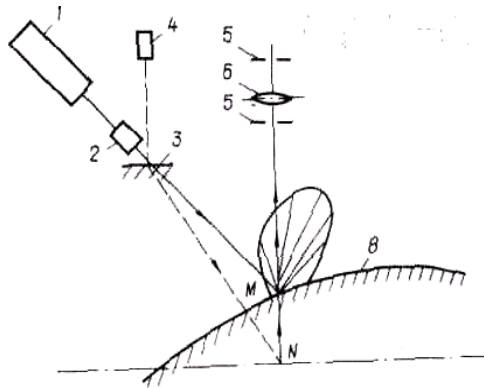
Схема прибора для контроля размерных параметров изделий
